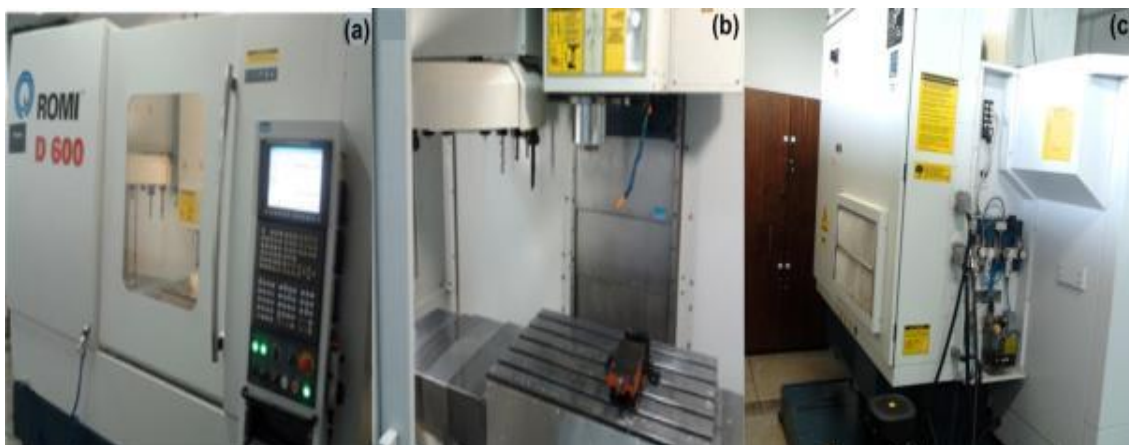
Máquina CNC Romi-D600 utilizada nos ensaios de usinagem: (a) parte frontal; (b) parte interna; (c) parte traseira
